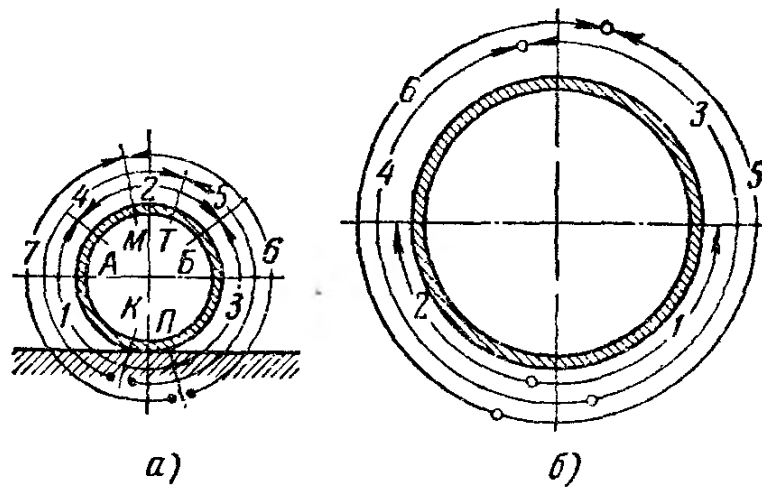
Схема сварки неповоротного стыка трубы
